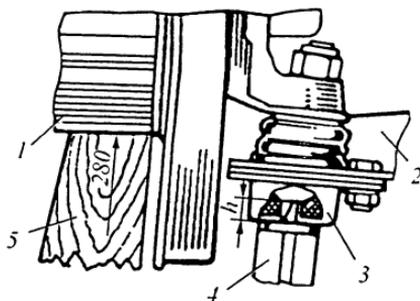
Проверка нижнего шарового шарнира передней подвески автомобиля: 1 — ступица колеса; 2 — нижний рычаг; 3 — нижний шаровой шарнир; 4 — штангенциркуль; 5 — деревянная колодка; h — измеряемое расстояние
